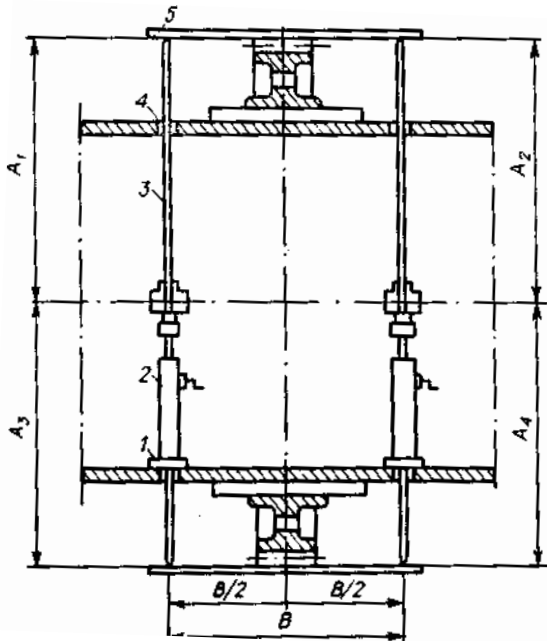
Центрування зубчастого вінця без повороту корпусу, що обертається, :
